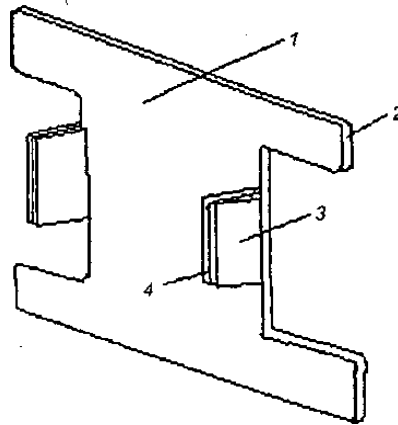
Регулювальна накладка буксового вузла візка вантажного вагона
